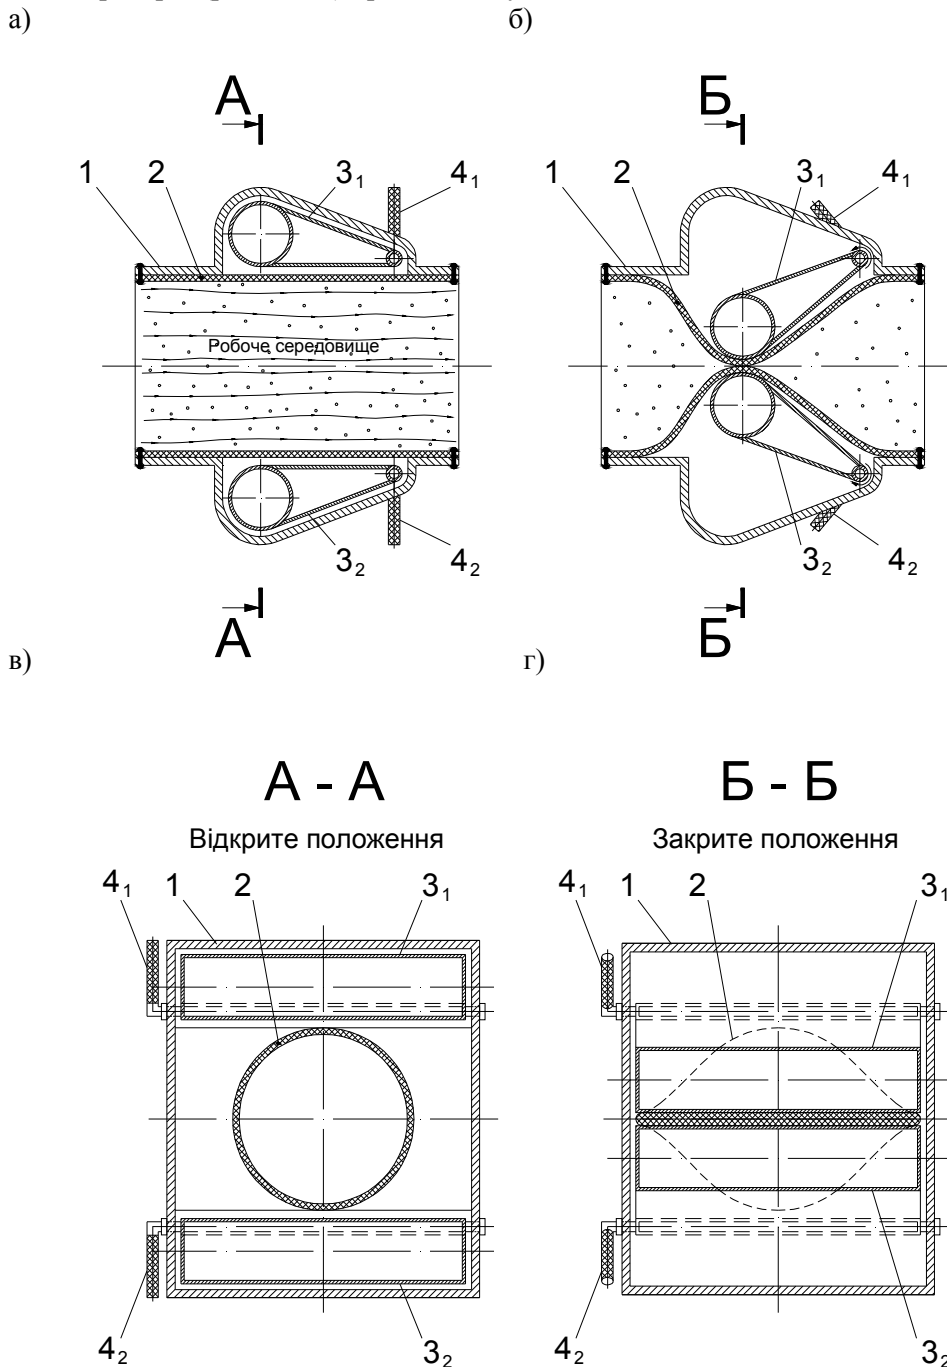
Дросельний пристрій з герметично закріпленою всередині корпуса еластичною розтягувальною вставкою, що переміщується регулювальними запірними елементами у вигляді двох барабанів
